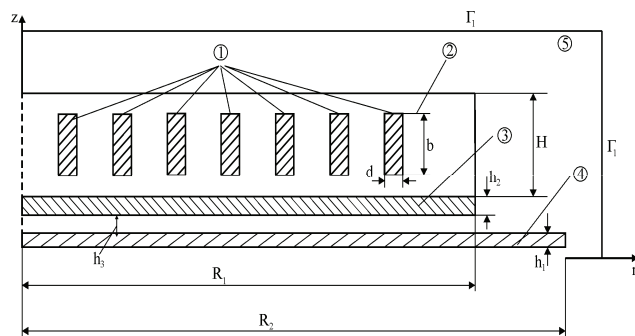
Розрахункова схема складеного багатовиткового індуктора із допоміжним екраном та заготовки: 1 – багатовитковий струмопровід; 2 – допоміжний екран; 3 – діелектричний бандаж; 4 – заготовка; 5 – оточуюче середовище (повітря)
